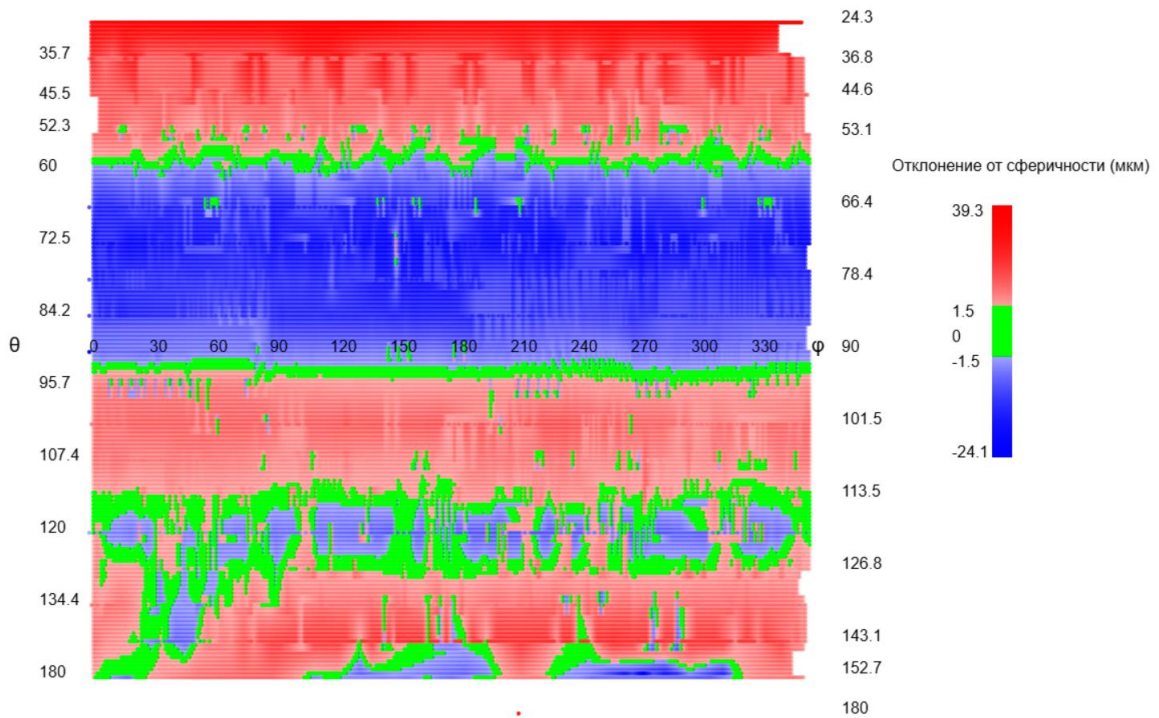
Развертка сферической поверхности шарового пальца №2 после притирки
